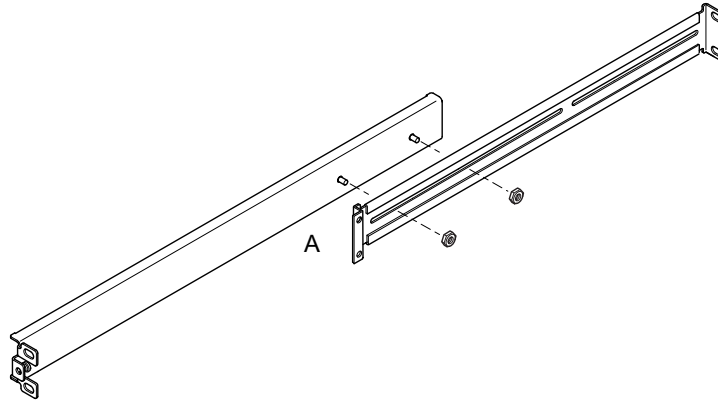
Placement des supports guidés pour un châssis standard de 19 pouces de largeur
